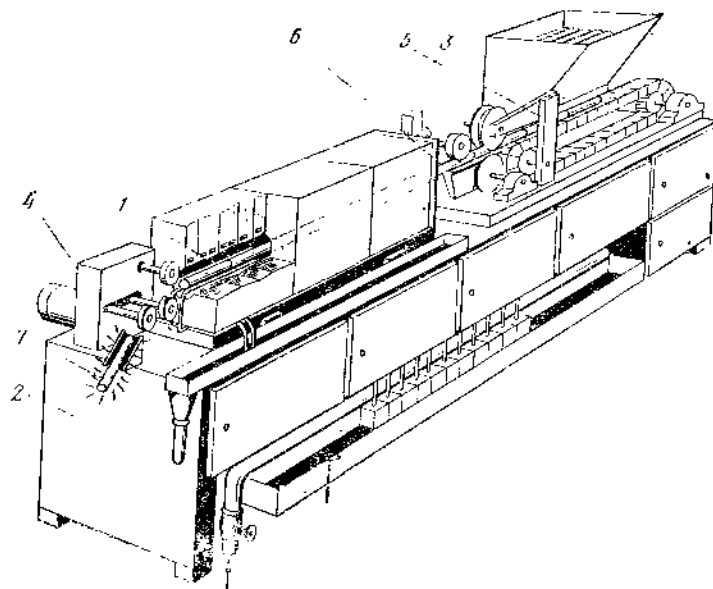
Индукционная установка для методического нагрева мерных заготовок
